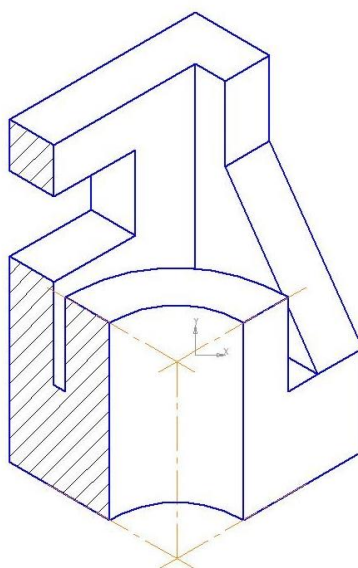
Чертеж детали с разрезом пополам относительно оси ОХ
